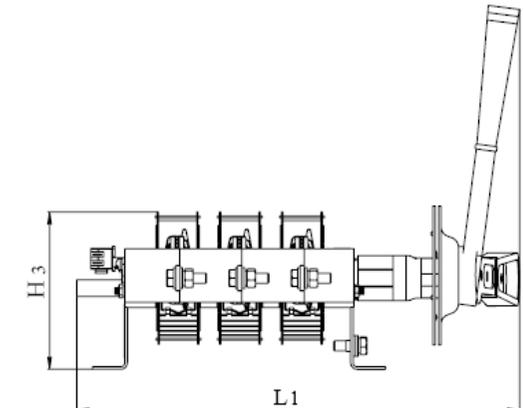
Выключатель-разъединитель трехполюсный на одно направление с боковой смещенной рукояткой.
